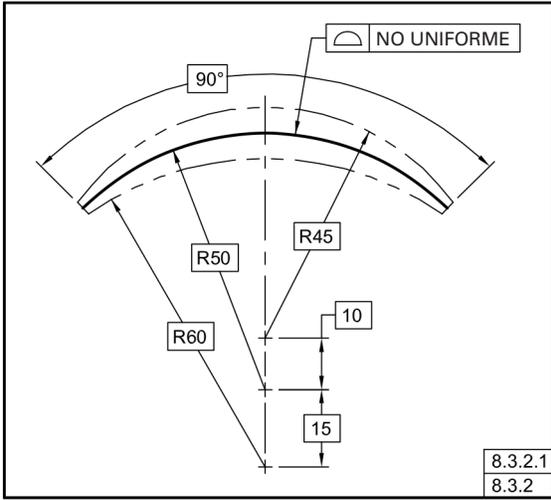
Zona de Tolerancia No uniforme de Perfil
